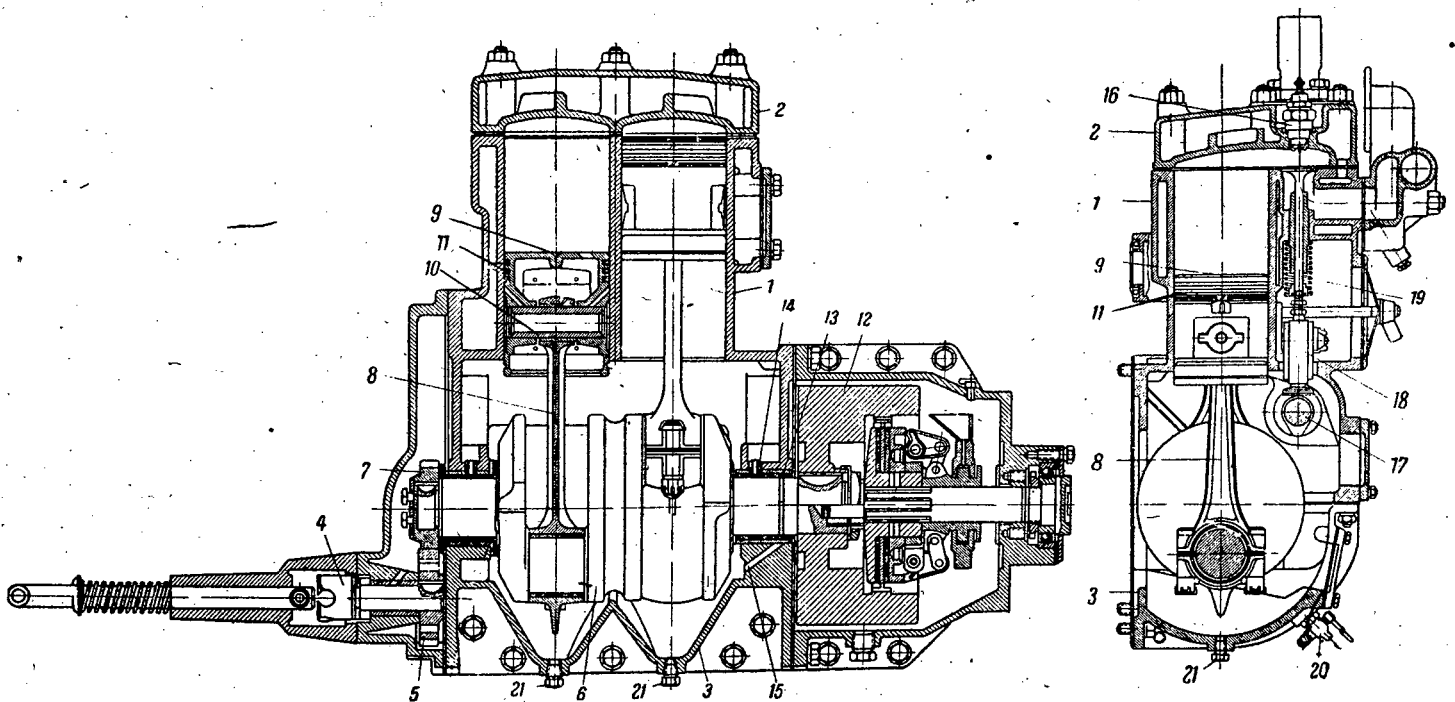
Продольный и поперечный разрезы пускового двигателя:
